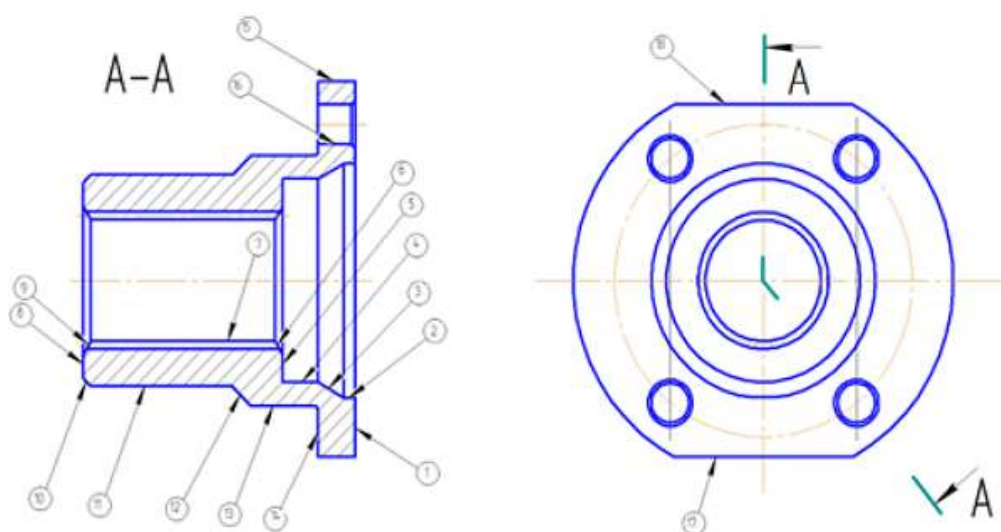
Ескіз деталі «Фланець КС-4574А-20.14» з нумерацією оброблюваних поверхонь
